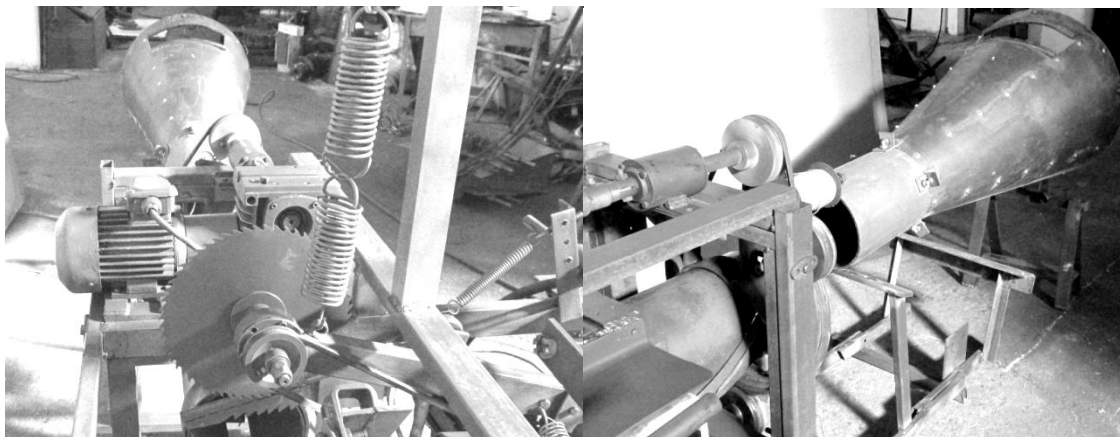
Загальний вигляд макетного зразка пристрою для безперервного пресування виноградної лози з конусоподібною пресувальною камерою
